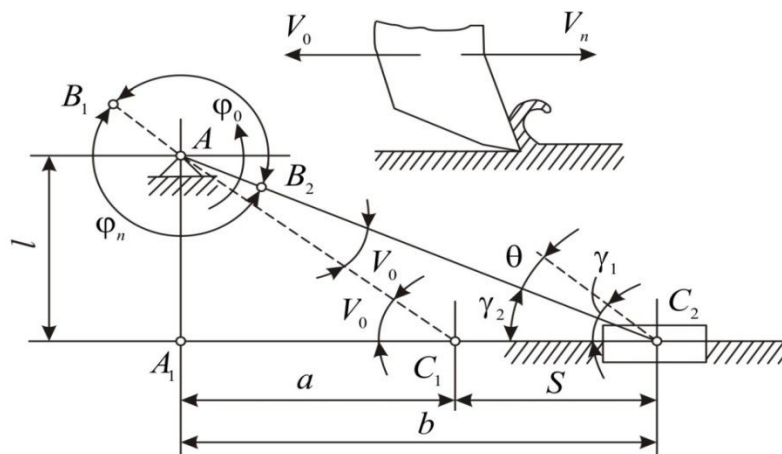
Внецентренный кривошипно-ползунный механизм
